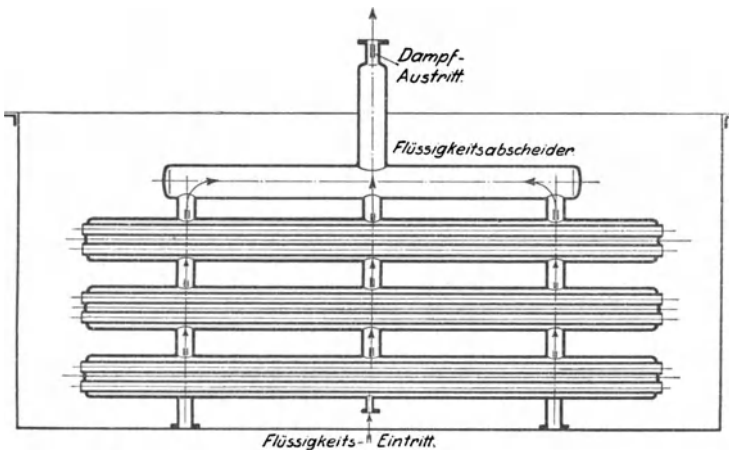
Elementen-Ammoniakverdampfer für Eiserzeugung. Gesellschaft für Lindes Eismaschinen AG., Wiesbaden.
